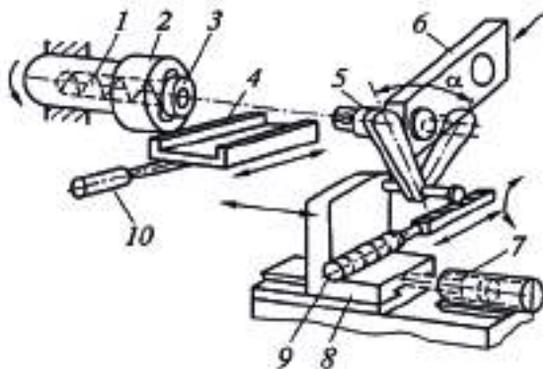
Устройство загрузки-выгрузки, встроенное в одношпиндельный токарный автомат: 1 – пружина; 2 – патрон; 3 – обработанная деталь; 4 – отводящий лоток; 5 – рука; 6 – подводящий лоток; 7, 9, 10 – гидроцилиндры; 8 – питатель
